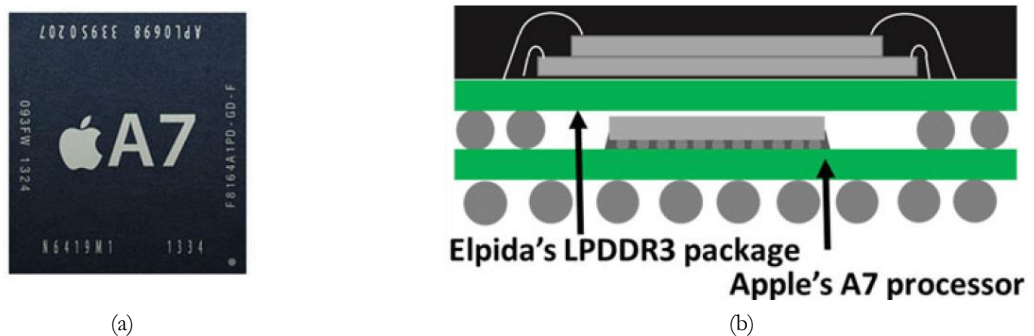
(a) Vue sur le dessus du packaging PoP Apple A7 et (b) schéma de la section de coupe de cette mise en boîtier [109]
